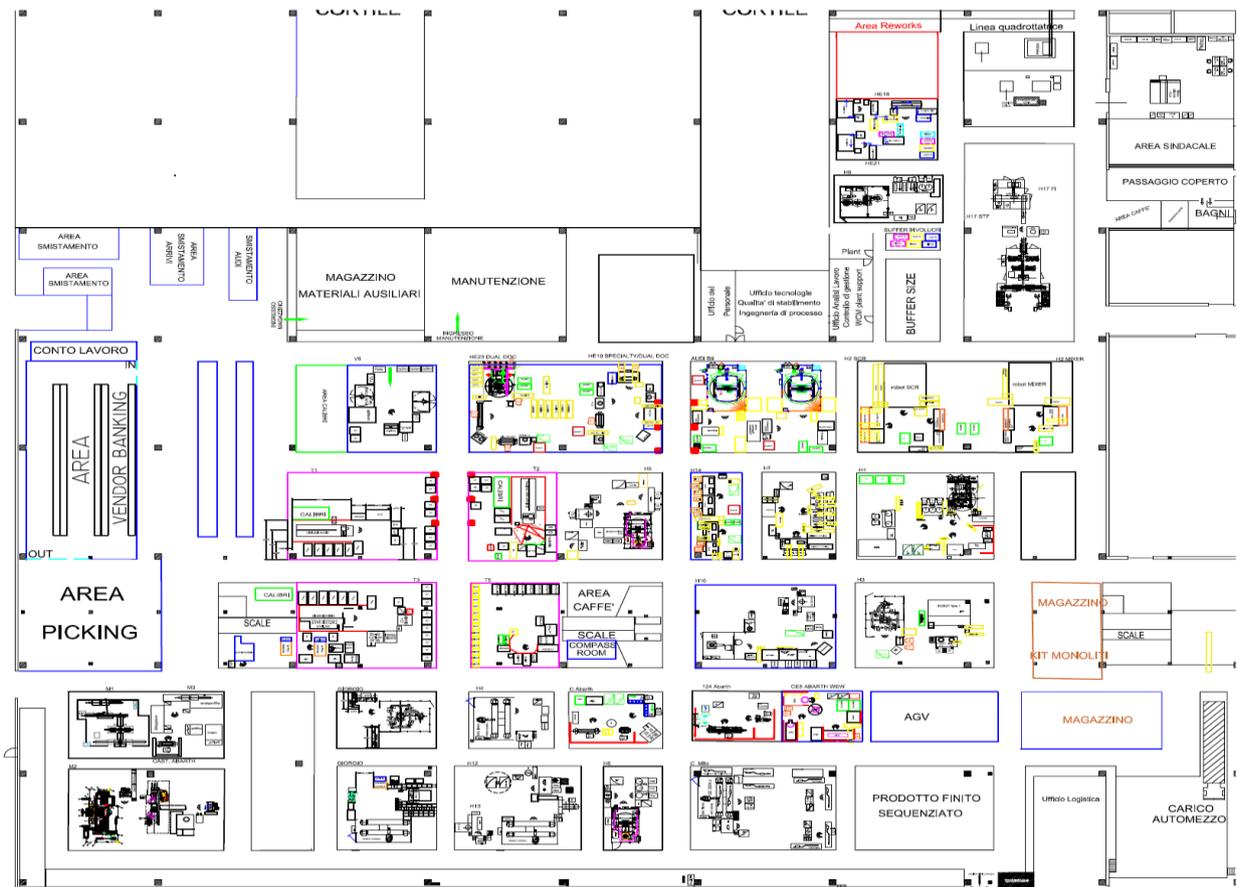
planimetria della sezione Exhaust System dello stabilimento della Magneti Marelli presso Venaria Reale (TO)
